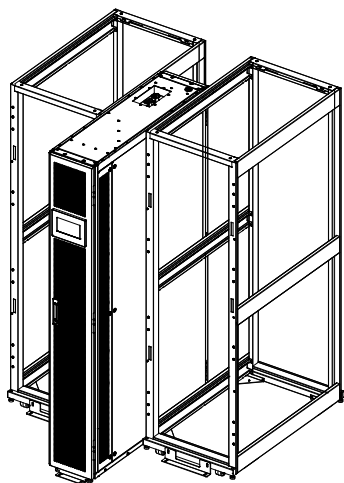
Panneaux latéraux perforés installés, Airblock avant installé
